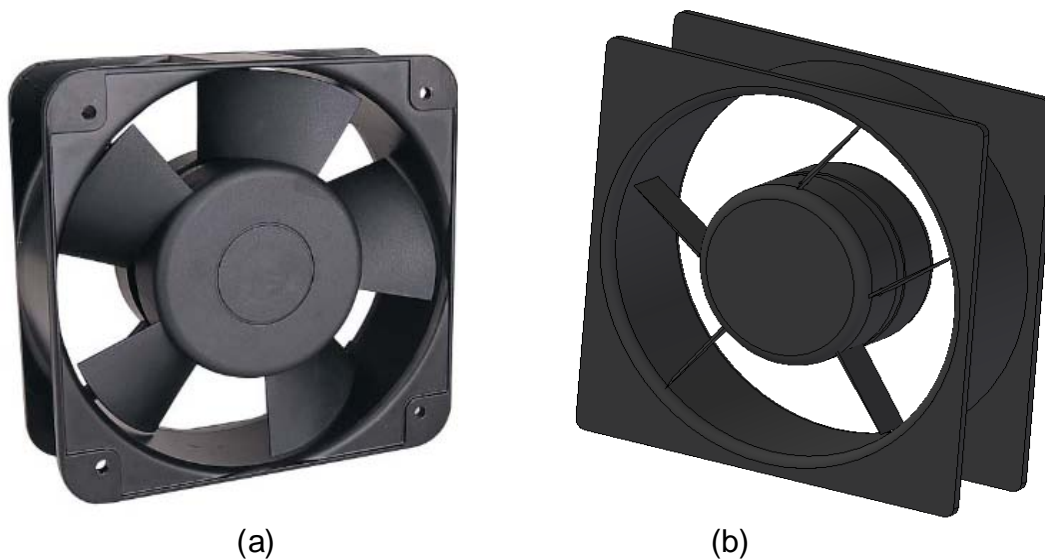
(a) Ventilador AC Axial Fans Fonsoning [33], (b) Diseño en Solid Edge
